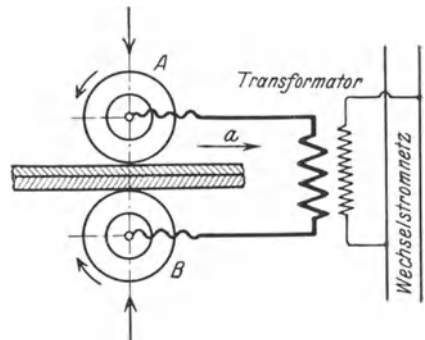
Schema der elektrischen Nahtschweißung.
